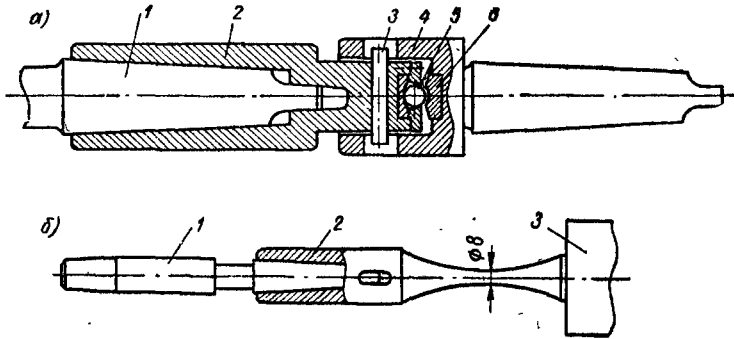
Шарнирная (а) и эластичная (б) оправки для разверток.
